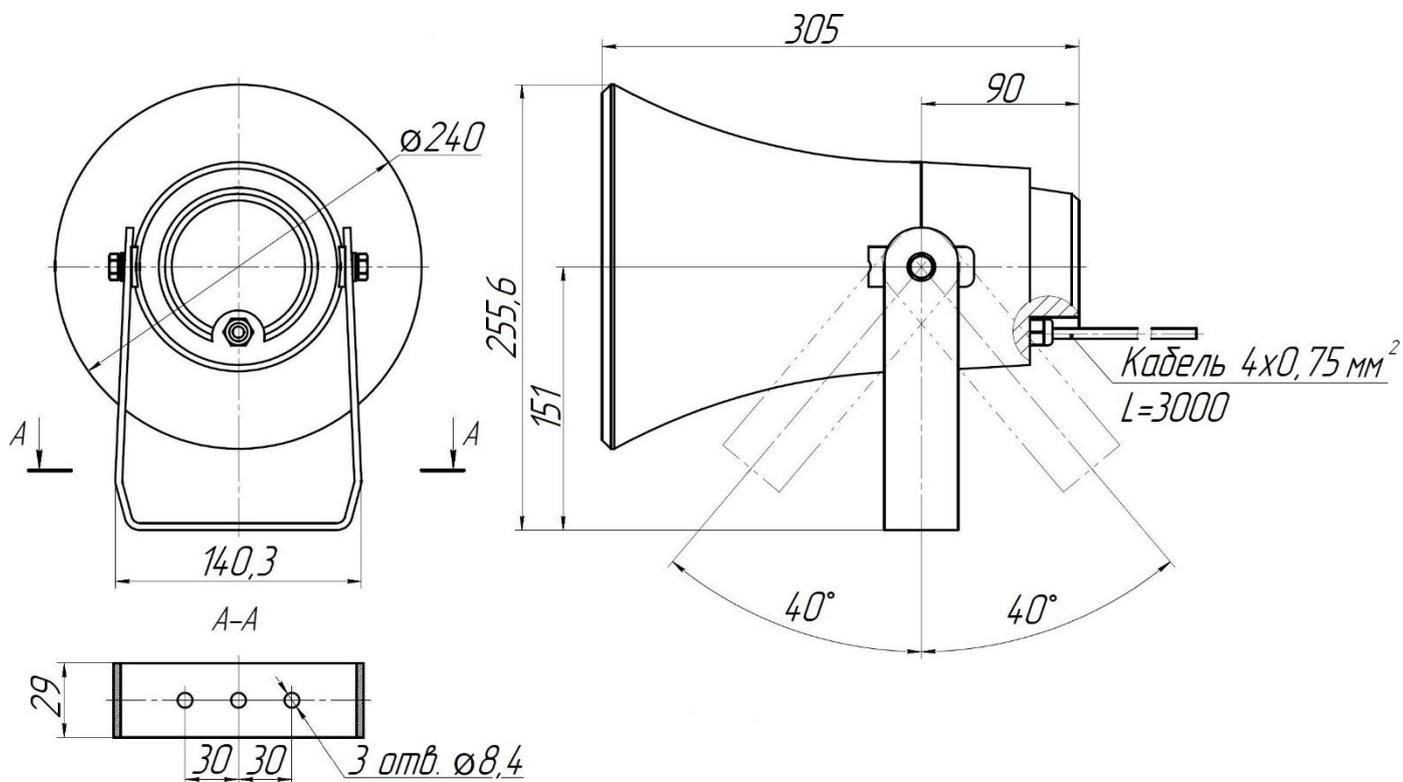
Габаритные и установочные размеры ГГ-3/100/30
